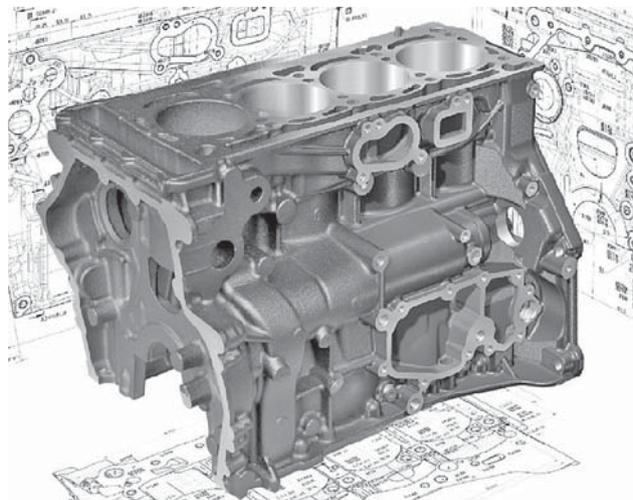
Отливка блока двигателя R4-TFSI-EA888 [6]
